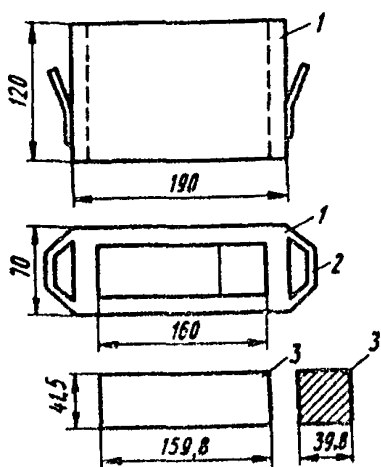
Форма для изготовления образцов-балочек: 1 - корпус; 2 - ручка; 3 - вкладыш
